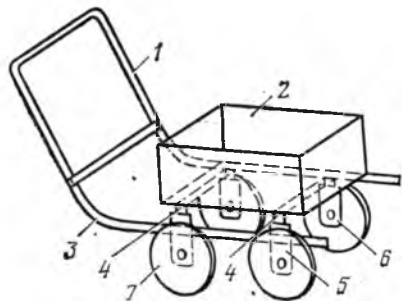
1 — ручка; 2 — ящик (или кузовок); 3 — полоз; 4 — опорная скоба; 5 — кронштейн колеса; 6 — цапфа; 7 — колесо
